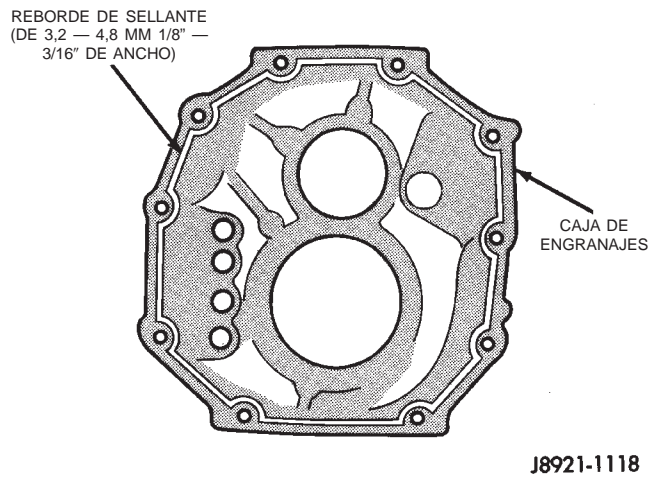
Aplicación de sellante en la caja de engranajes de la transmisión
